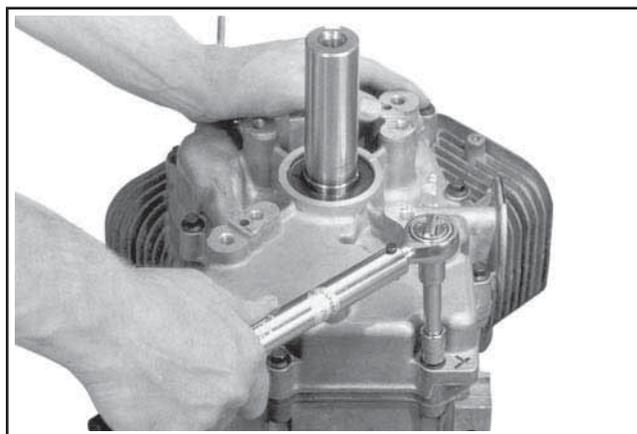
Serrage des raccords de la plaque de fermeture.
